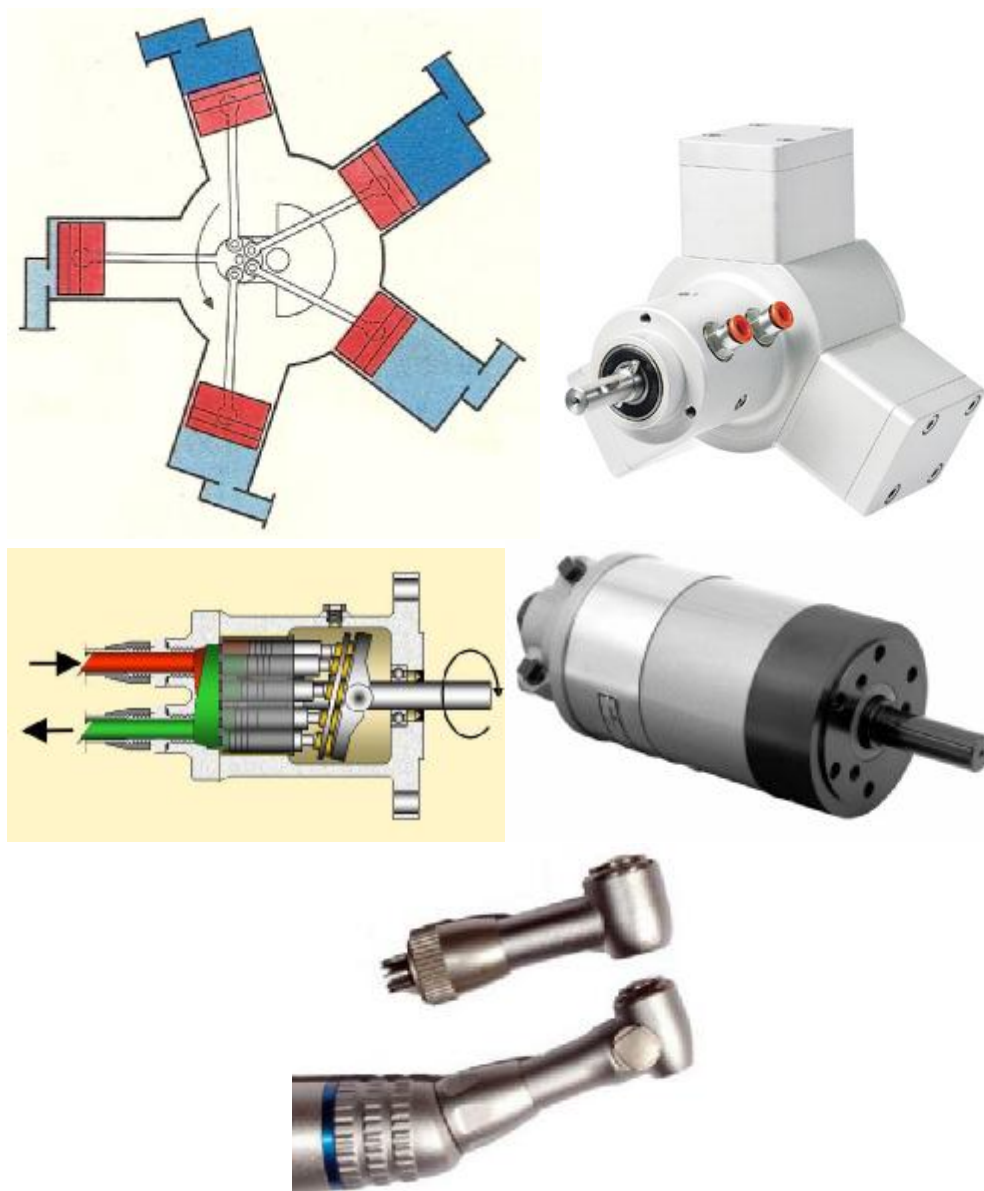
Motores pneumáticos de pistões radiais, de pistões axiais e turbo motor.
